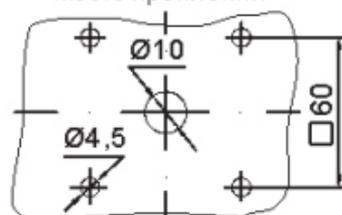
Габаритные, установочные, присоединительные размеры кулачковых переключателей 4G40, 4G63, 4G80, 4G63/100 открытого исполнения
